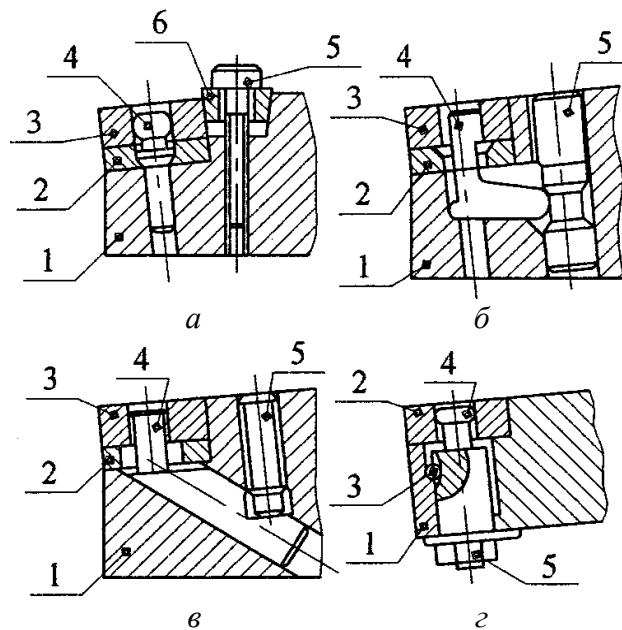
Основні конструкції кріплення БНП з циліндричним отвором
